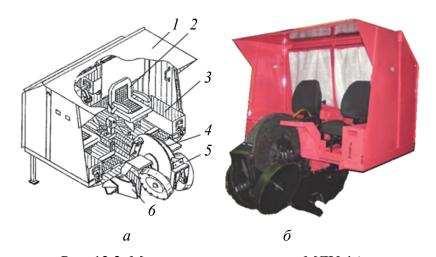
Машина лесопосадочная МЛУ-1А: a — схема устройства; δ — общий вид агрегата; l — рама с ограждением; 2 — сиденье; 3 — ящик для посадочного материала;
